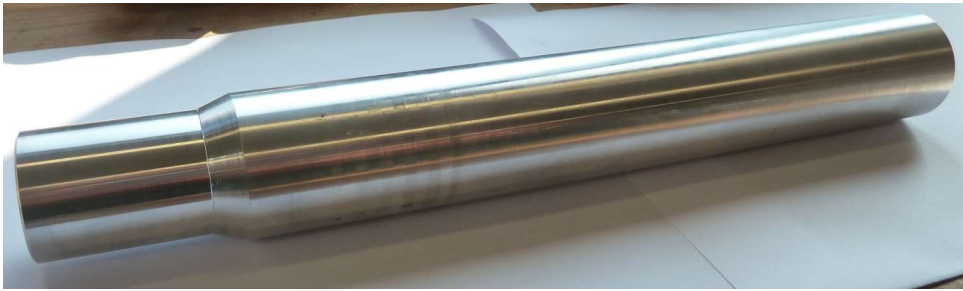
Gefertigtes Gehäuse des neuen Werkzeugträgers
